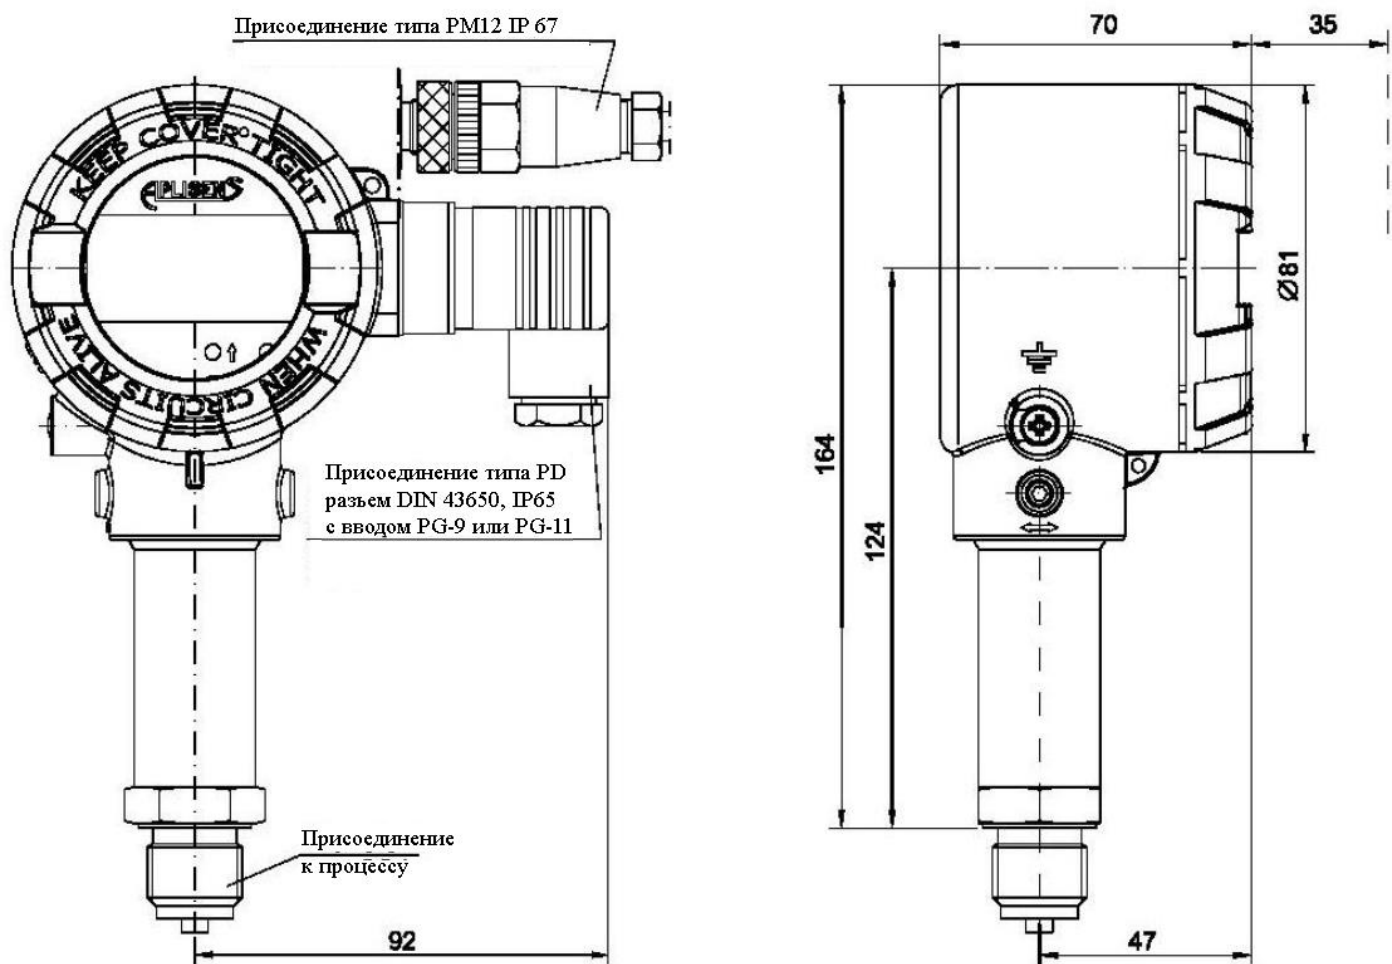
с. Преобразователь РС-28 с присоединением типа ALM
